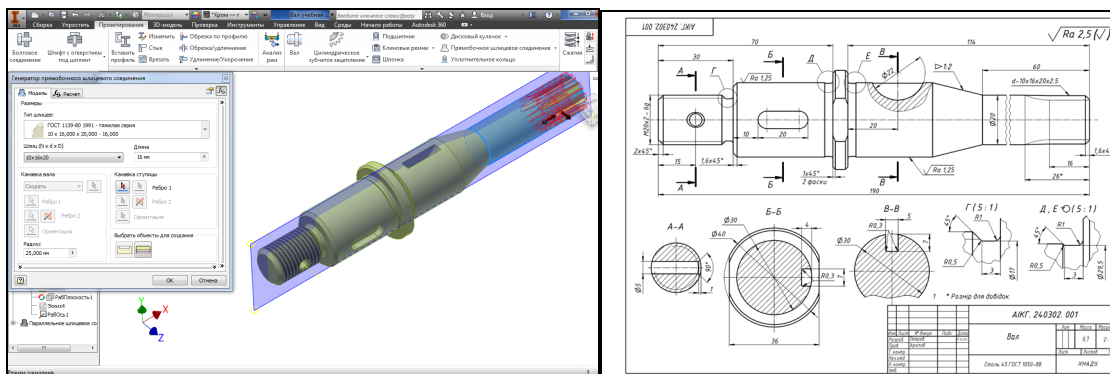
Модель та робочий кресленник деталі "Вал шліцьовий".
